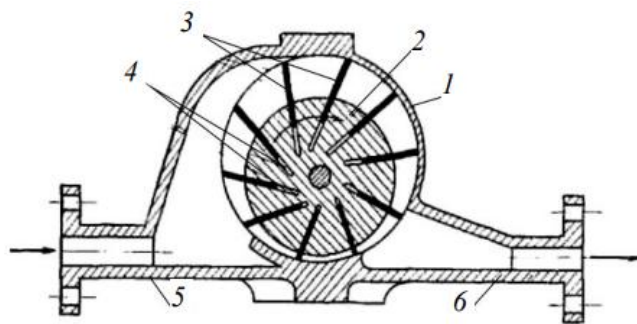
Роторний компресор пластинчастого (шиберного) типу:
